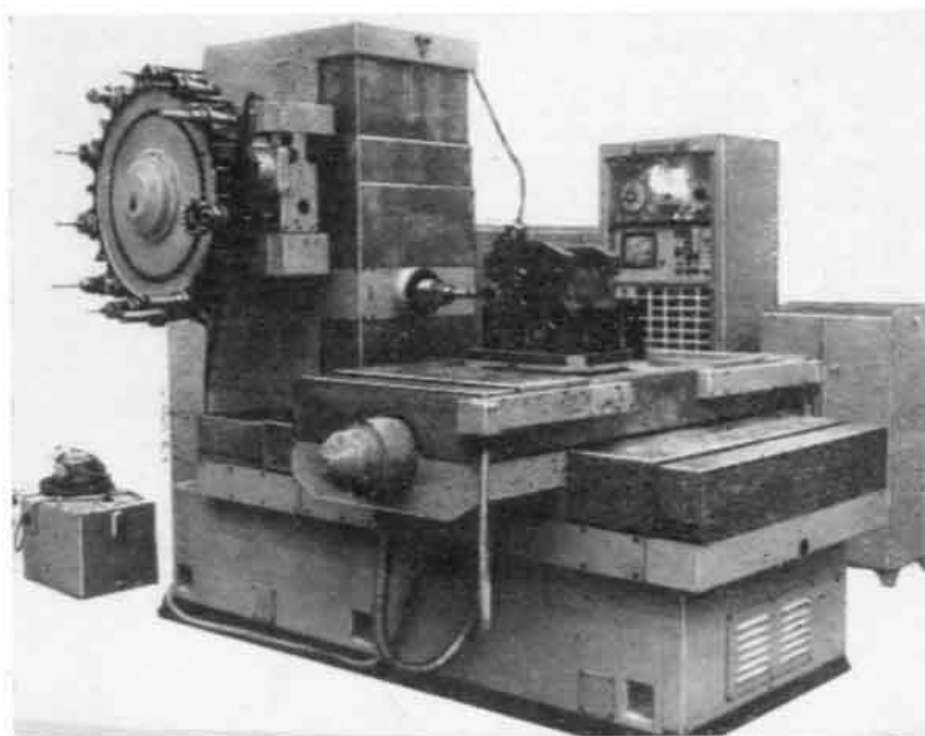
Горизонтальный станок с магазином типа «*РУКА*» и барабаном с инструментами
